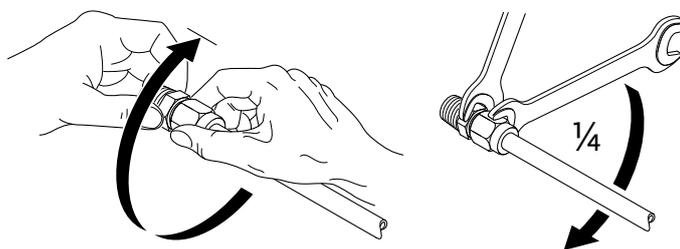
1/4 de rotação adicional da abraçadeira de ligação
